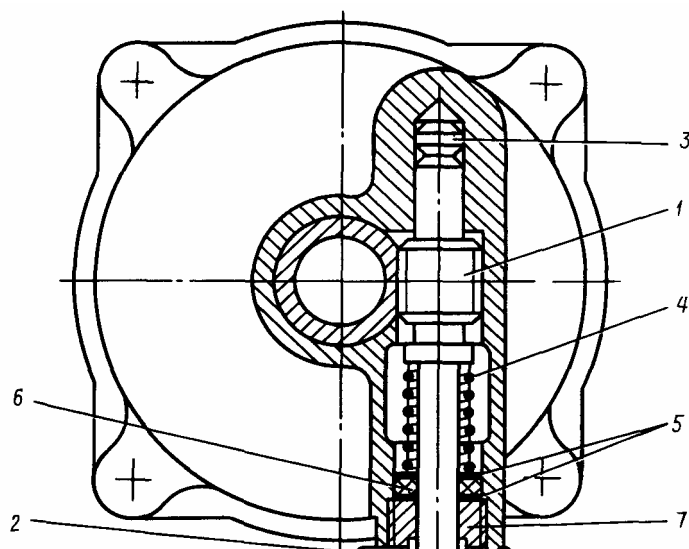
Конструктивный разрез регулятора Р-2 сер. 04
